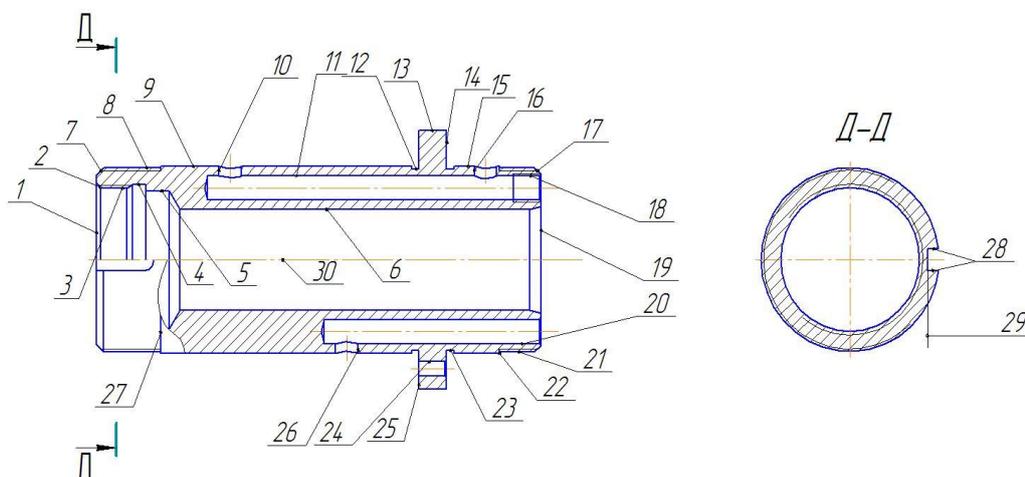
Кодировка поверхностей детали "Обойма штока"
